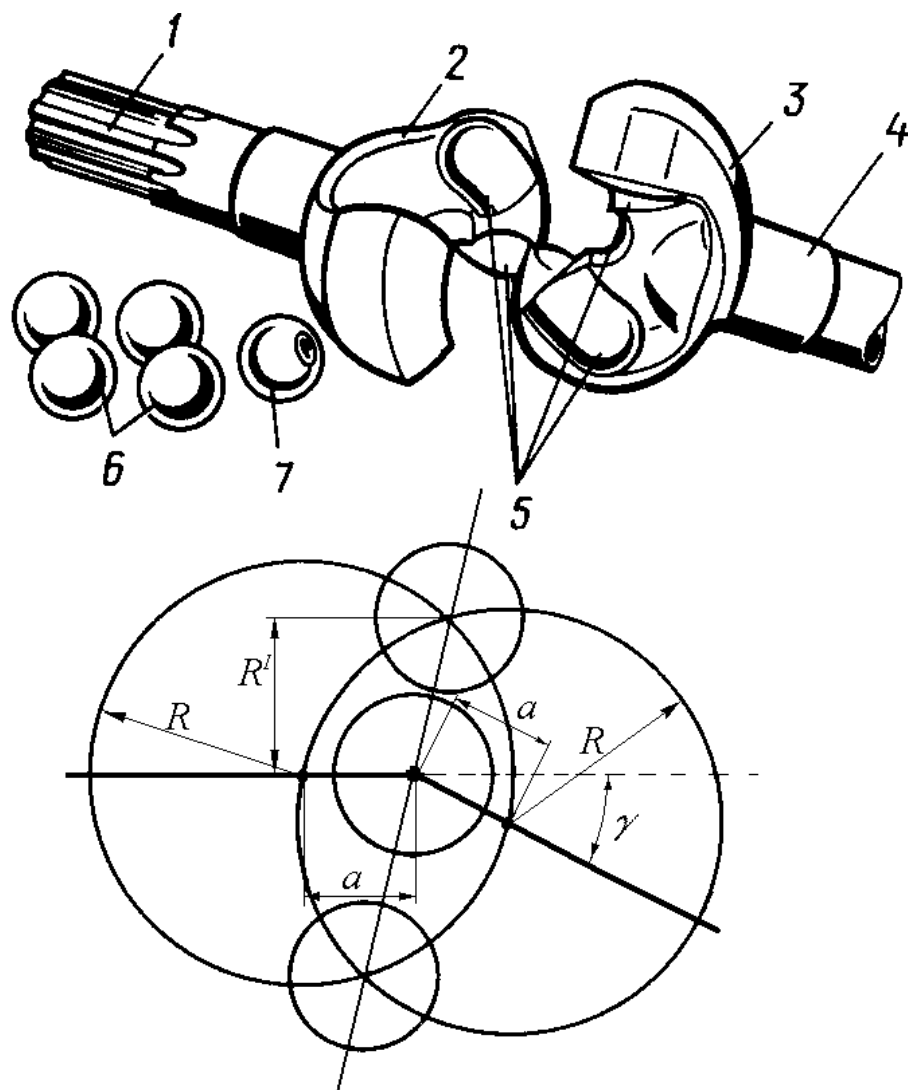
Четырехшариковый карданный шарнир с делительными канавками типа “Вейс”
